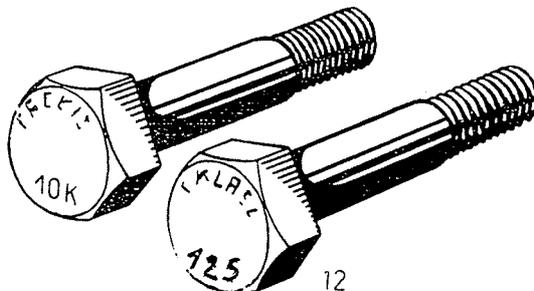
Kennzeichnung des Schraubenwerkstoffes
